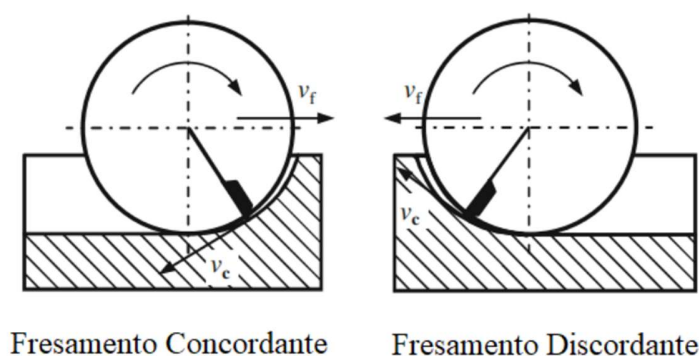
Esquemática de fresamento concordante e fresamento discordante (KLOCKE; KUCHLE, 2011).
